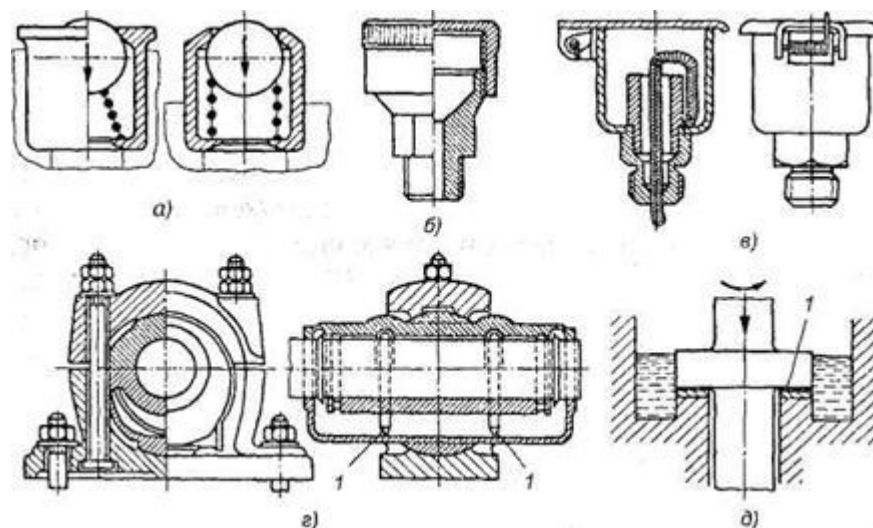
Способы смазывания подшипников: *а* — масленка с шаровым клапаном; *б* — колпачковая масленка; *в* — масленка с фитилем; *г* — смазывание кольцом; *д* — смазывание окунанием
